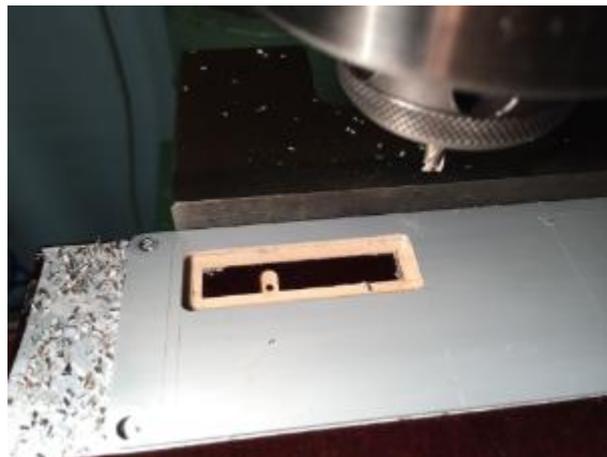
Fräsen des Ausschnitts für das Messinstrument
